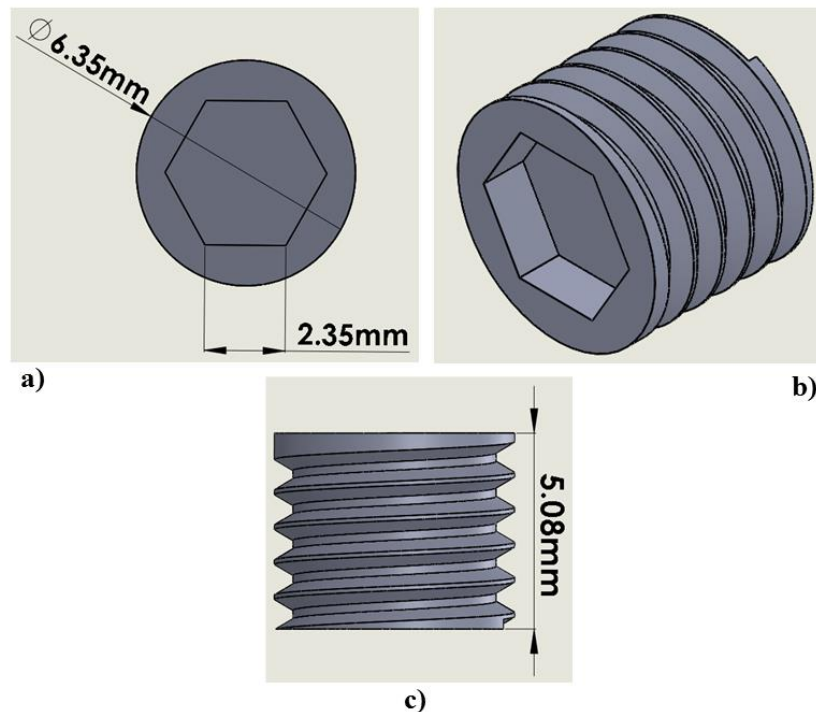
a) Vista superior del opresor con cabeza hexagonal interna, b) Vista isométrica del opresor, c) Vista lateral del opresor mostrando su longitud.
